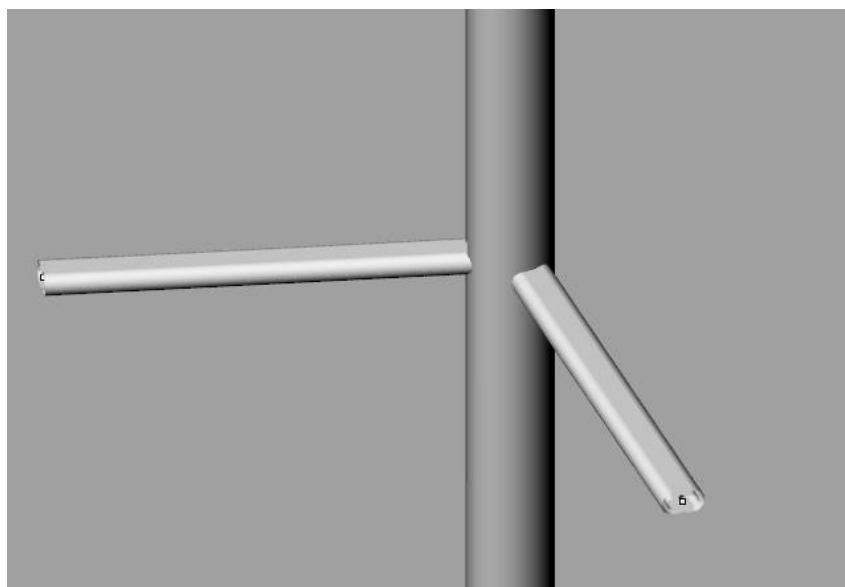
128 Vista detalle crucetas mástil formato 3D (Fuente: Propia)
